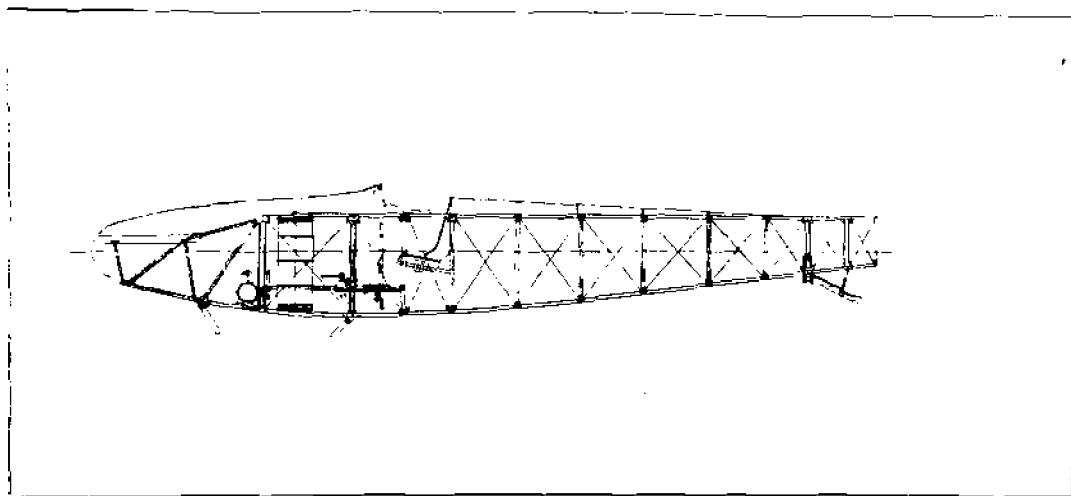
STRUTTURA DELLA FUSOLIERA CON CASTELLO MOTORE SMONTABILE
